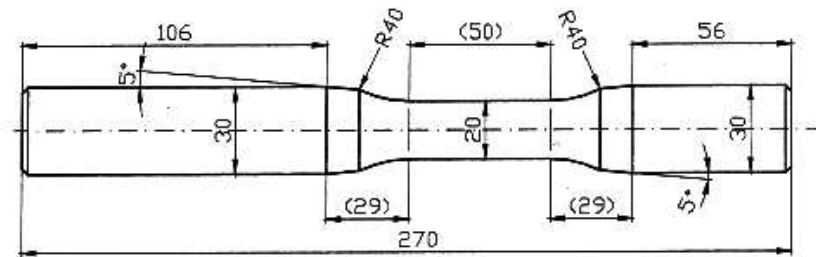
Eprouvette de flexion-torsion (dimension en millimètres) [72]
